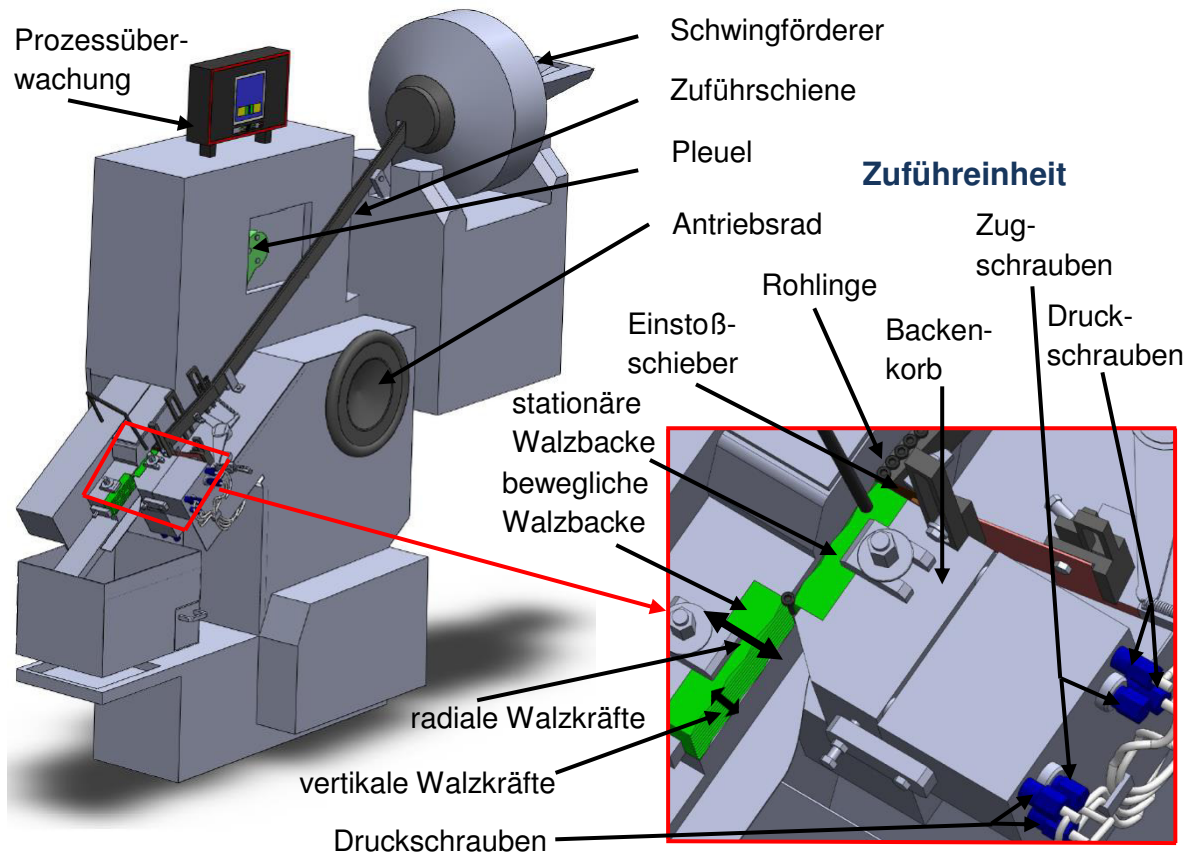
Aufbau des Walzsystems mit einer Detailansicht der Zuführeinheit
